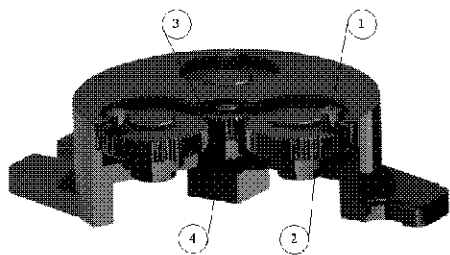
Переналагоджуваний базуючий модуль для установки корпусних деталей за площиною
